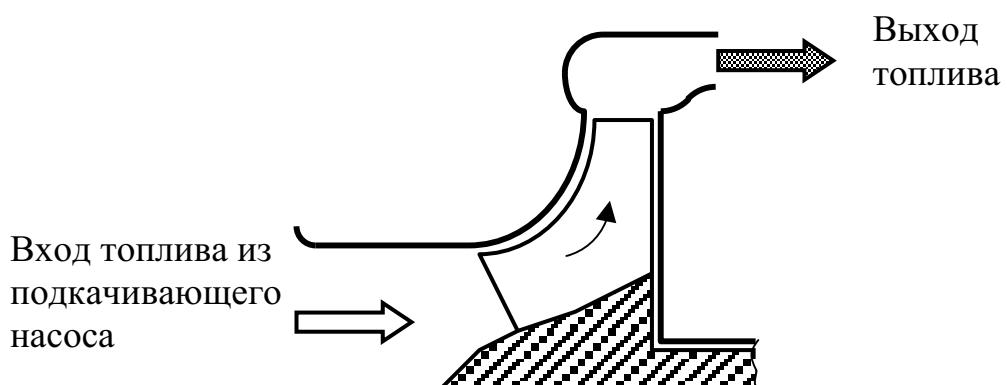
Схема центробежного топливного насоса высокого давления с крыльчаткой открытого типа
